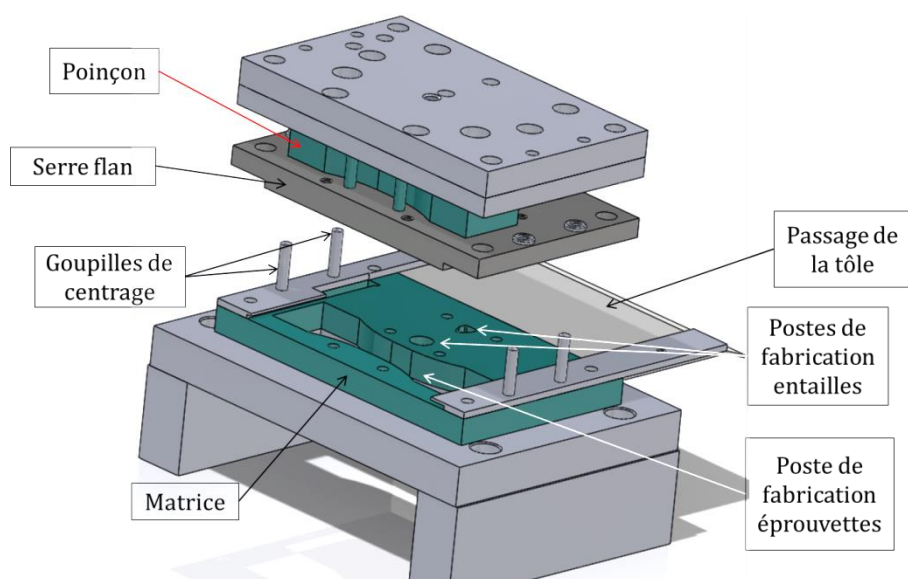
Outil utilisé pour la fabrication des éprouvettes de fatigue lisses et entaillées
